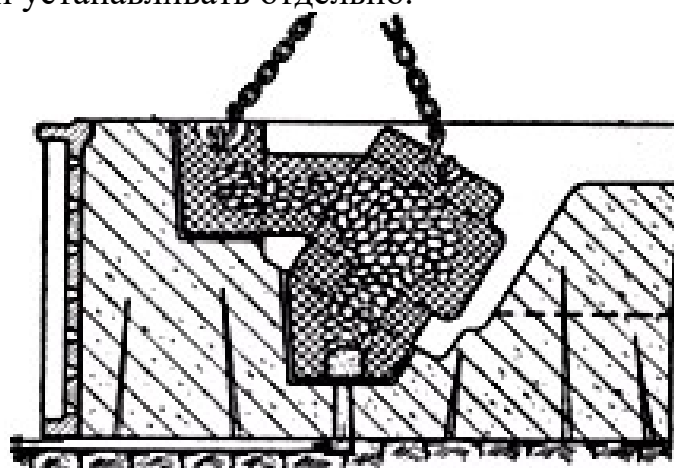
Установка в форму стержня, имеющего горизонтальный и вертикальный знаки
